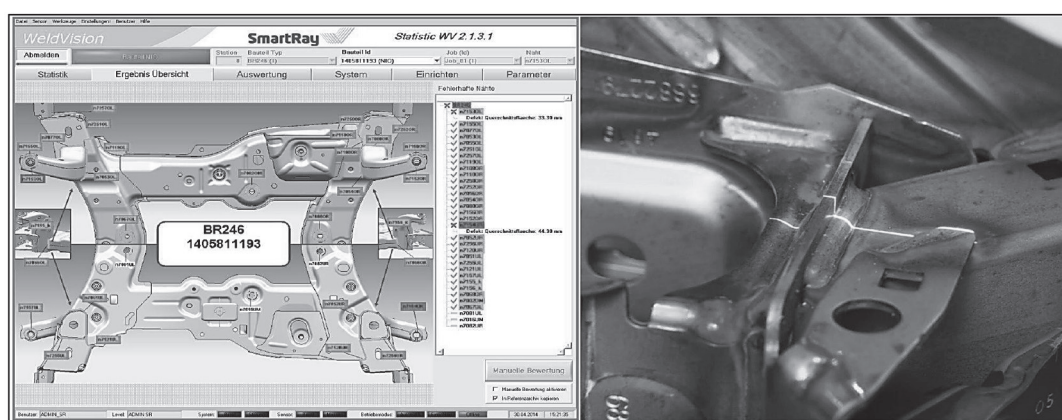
Sistem automatizat de verificare NDE Josy 3D Weld Inspection prin triangulație laser [7,8]
